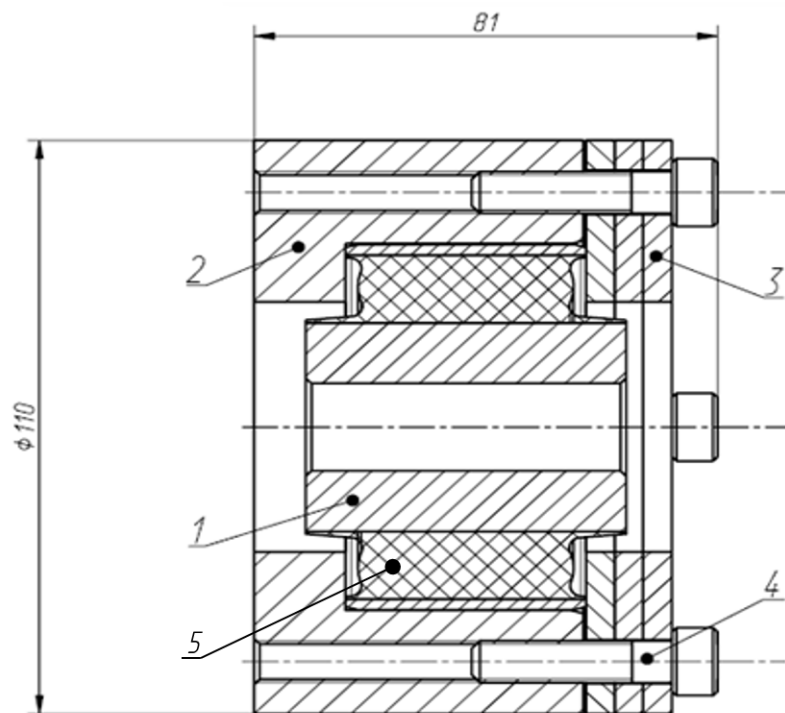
Общая схема виброгасителя: 1 – втулка, 2 – корпус, 3 – пластины, 4 – крепежные элементы, 5 – резиновый шарнир
